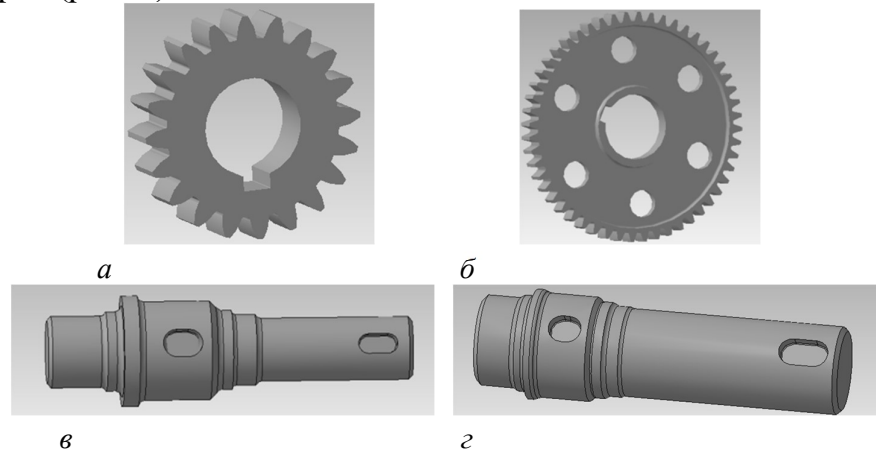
3D моделі деталей редуктора: *а* – шестерня; *б* – зубчате колесо; *в* – бистрохідний вал; *г* – тихохідний вал
